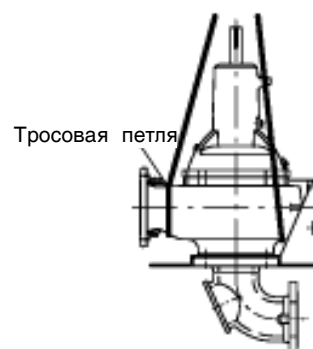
Транспортировка насосного агрегата в сборе (тип установки V)
